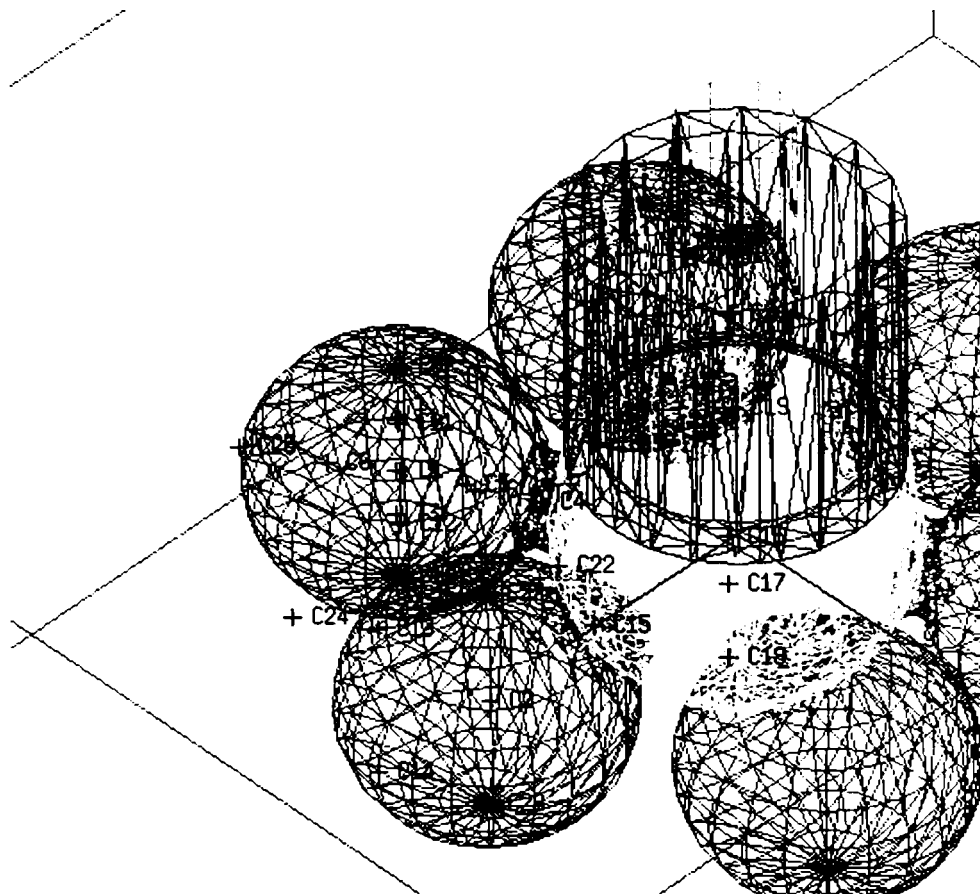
Discretizarea geometriei forme de turnare, desenată în CAD
